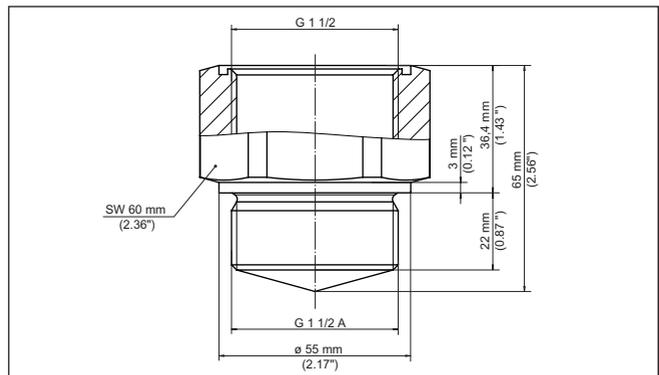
Dimensiones adaptador de rosca G1½ (DIN 3852-X) en rosca G1½, G2 (DIN 3852-X)
